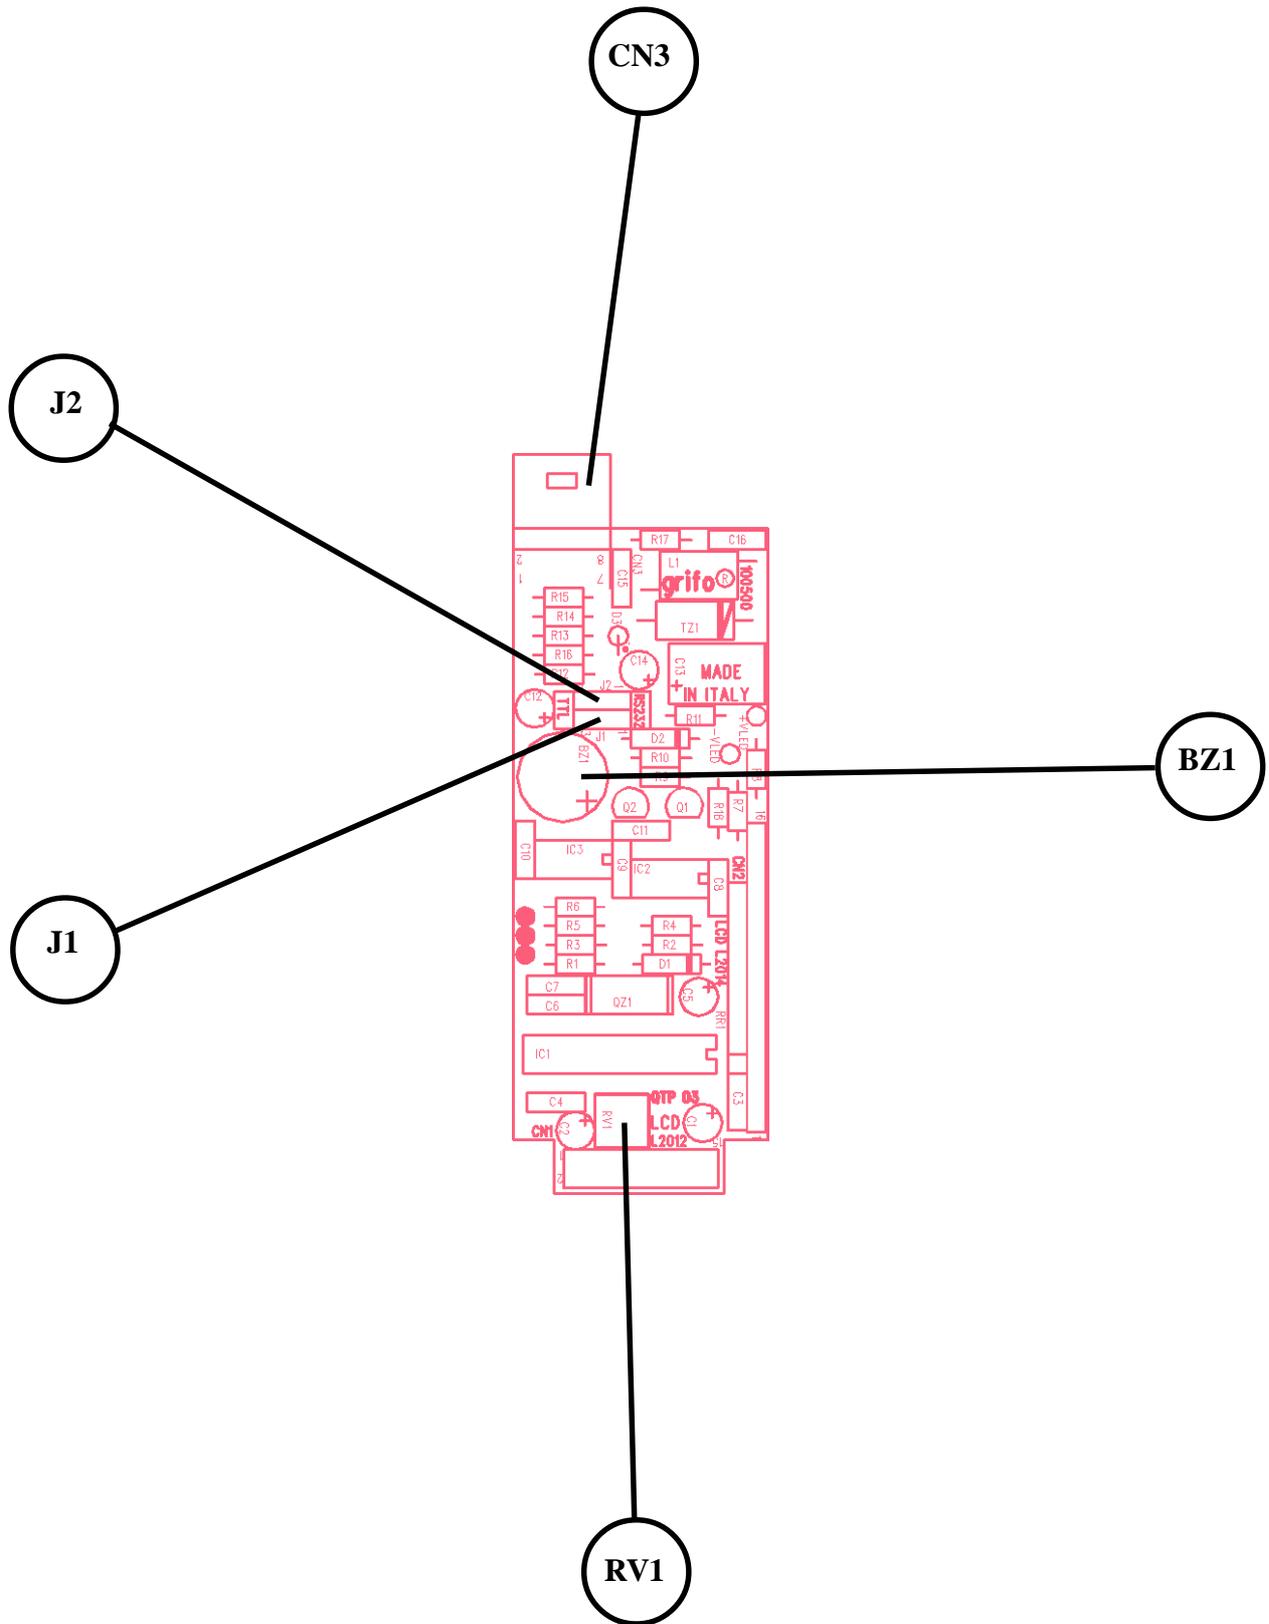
DISPOSIZIONE JUMPERS, CONNETTORI, TRIMMER, ECC.
